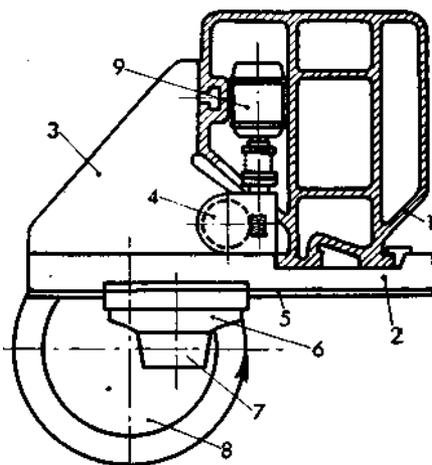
1, montante; 2, traviesa; 3, escuadra; 4, tuerca y husillo de elevación; 5, guías para el carro portaherramientas; 6, carro portaherramientas; 7, torre portaherramientas; 8, plato; 9, motor.
